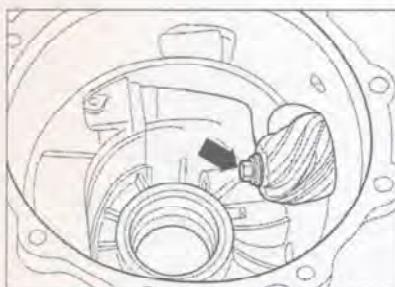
Вверните болт М10x40 в ведущую шестерню (стрелка) и прокрутите вторичный вал на 8 оборотов.
